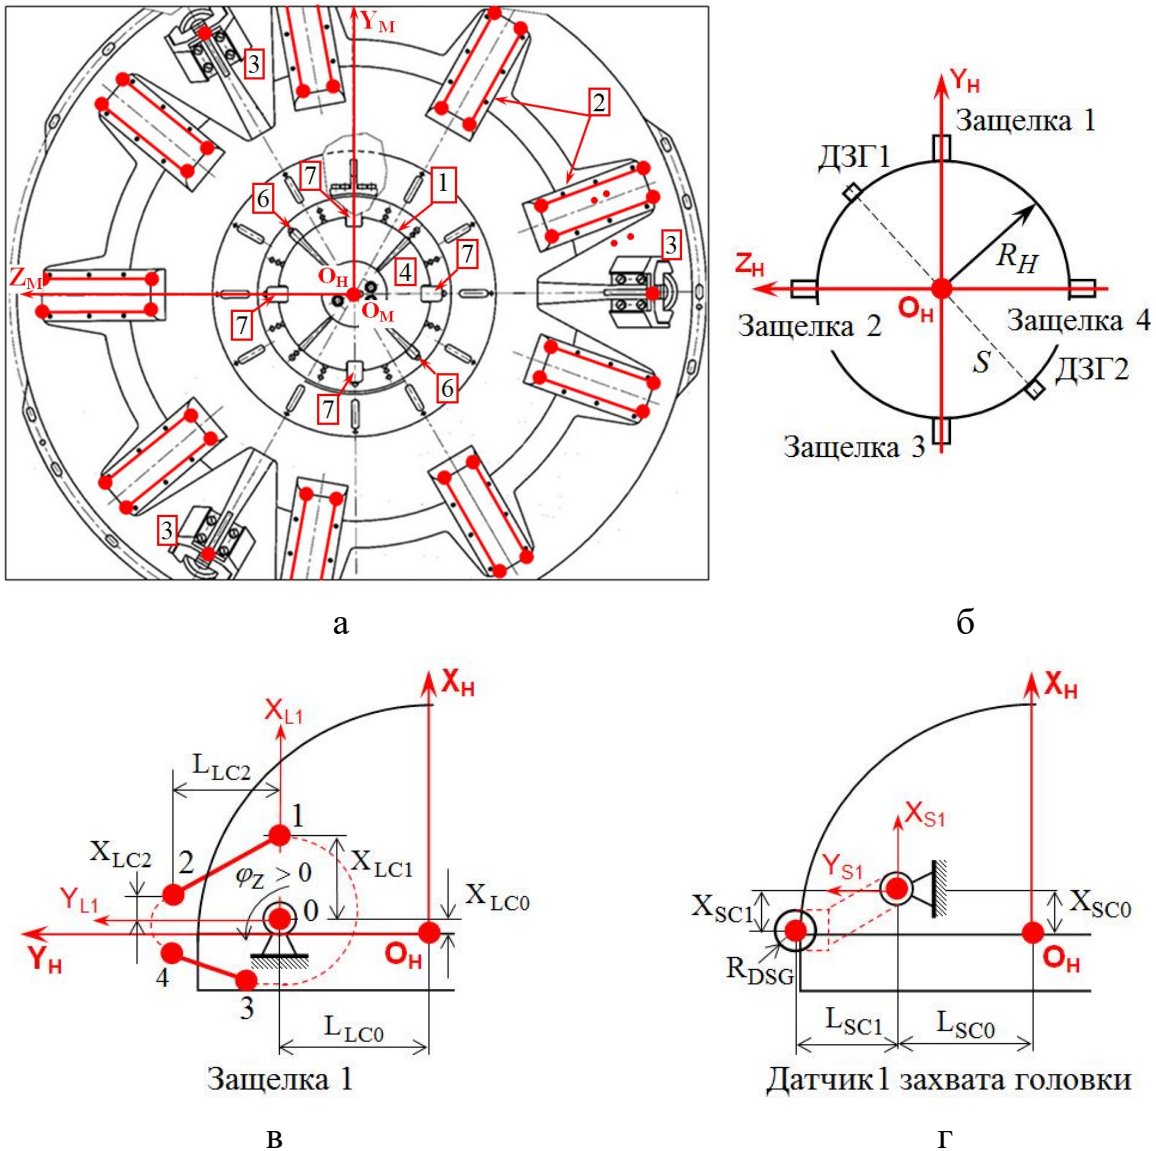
а) Системы координат, характерные точки и отрезки подвижного корпуса стыковочного механизма центрального типа, б) головки штыря, в) защелки 1, г) датчика 1 захвата головки (ДЗГ1)
